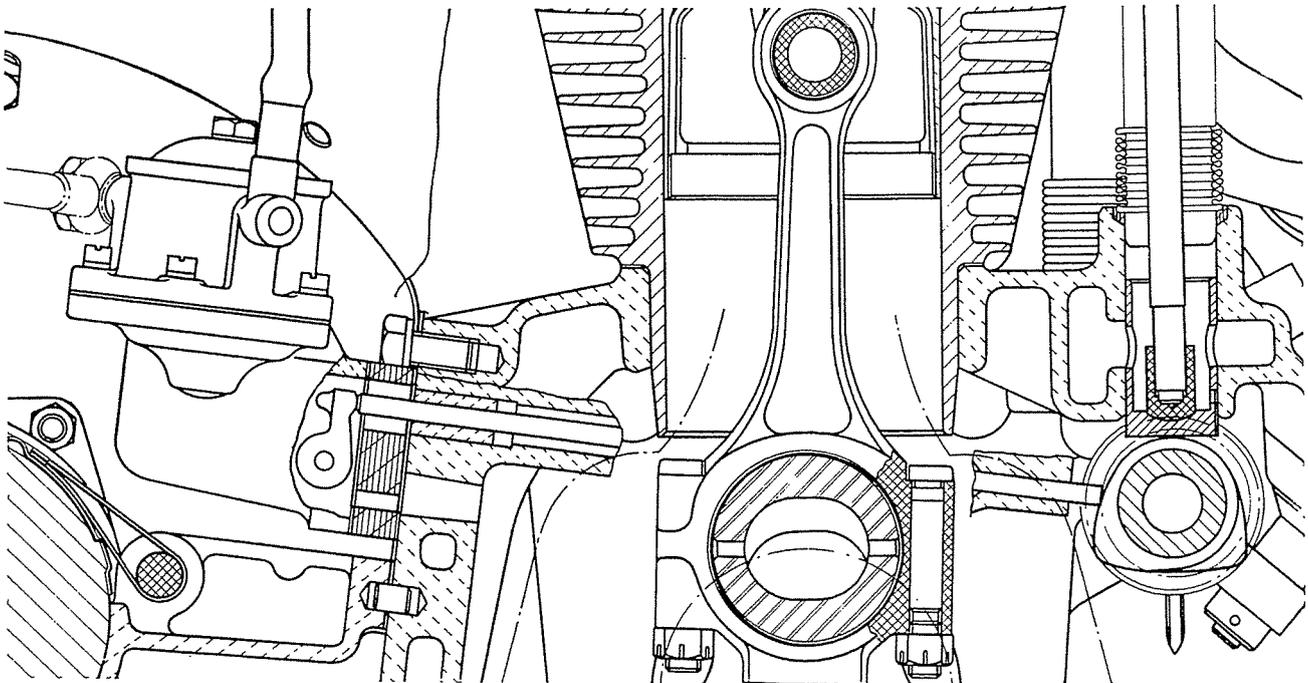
Querschnitt des Motors durch einen Ventilstößel und den Kraftstoffpumpenantrieb.
